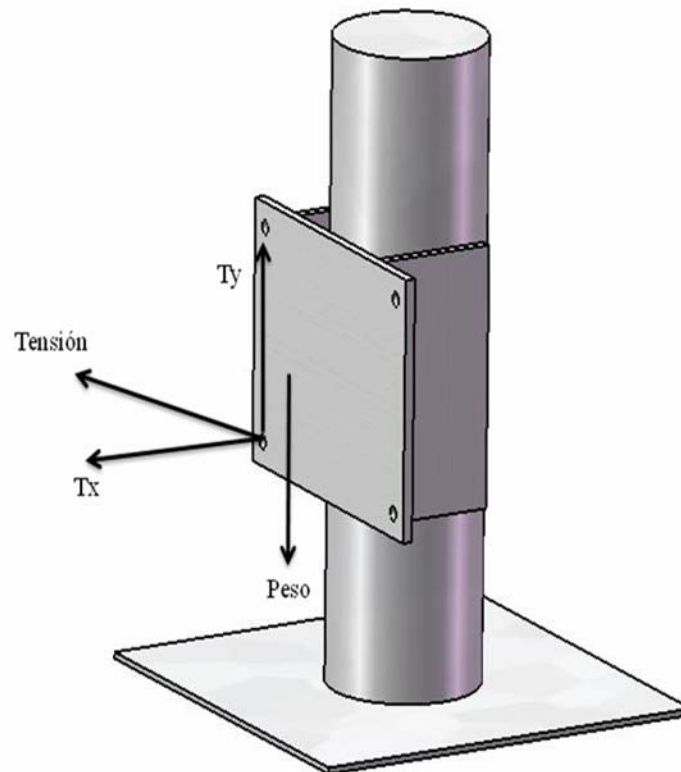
Unión de las planchas laterales y la plancha frontal. [Fuente propia]
